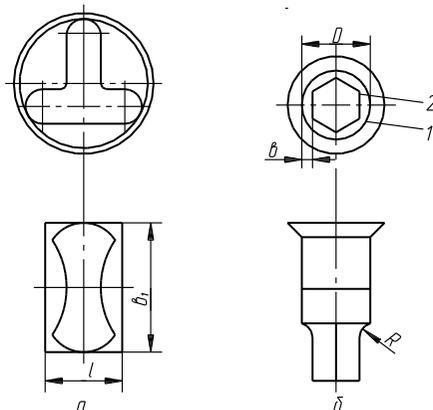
Конструкции пуансонов сложной формы: 1 — контур посадочной поверхности, 2 — контур рабочей поверхности
